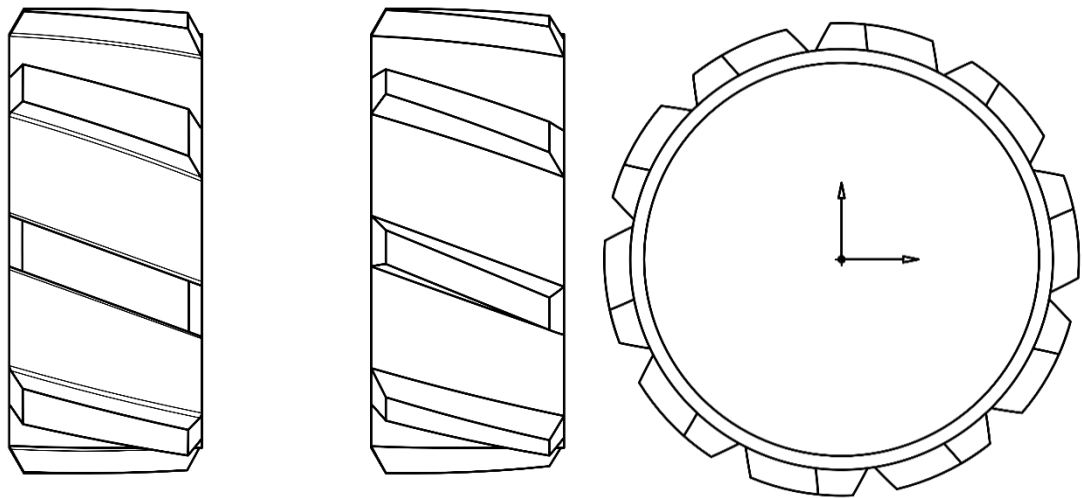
Профили лопастей колеса центратора 7 (слева) и 8 (центр);
